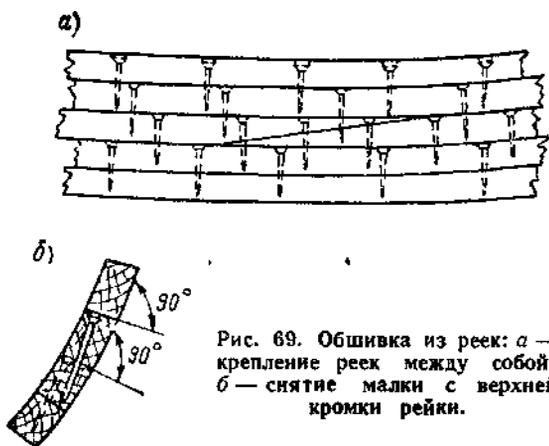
Обшивка из реек: а — крепление реек между собой; б — снятие малки с верхней кромки рейки.
